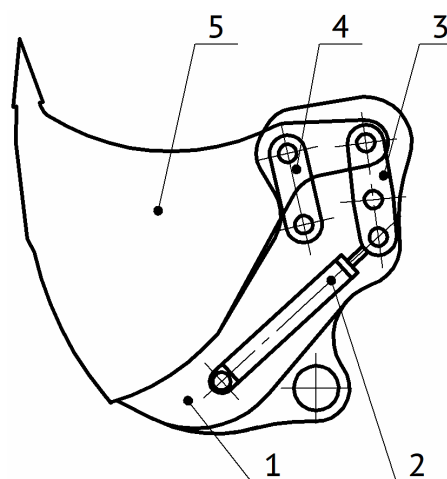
Предлагаемая конструкция механизма раскрытия ковша: 1 – основание ковша; 2 – гидроцилиндр открывания; 3 – двуплечий рычаг; 4 – коромысло; 5 – козырёк
